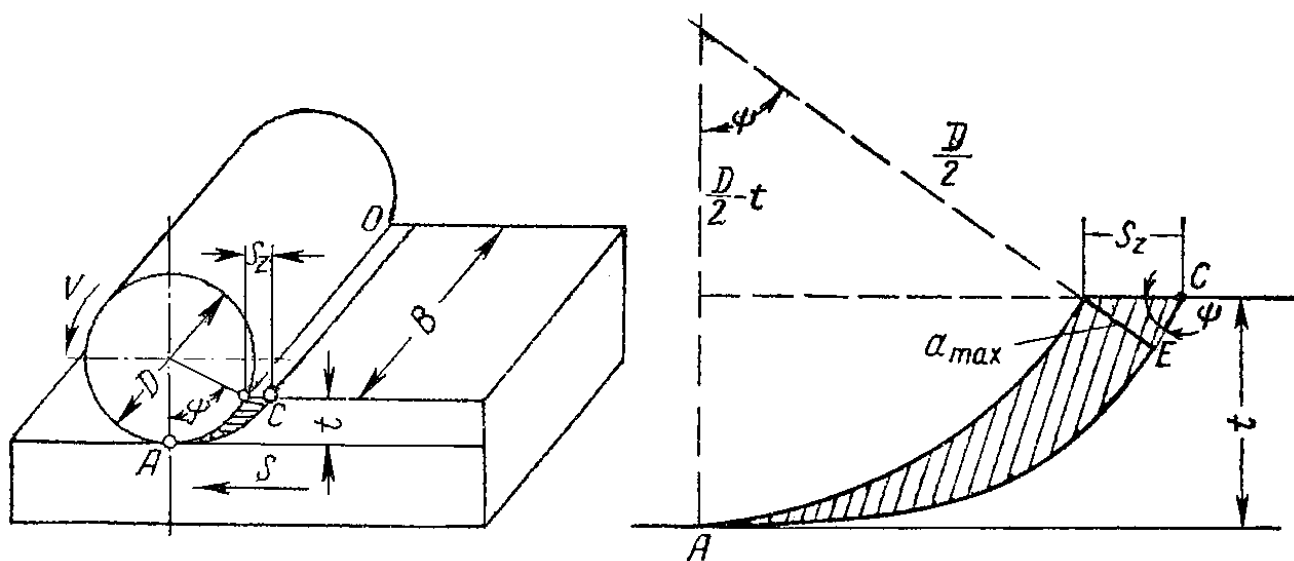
Схема работы цилиндрической фрезы с прямыми зубьями
